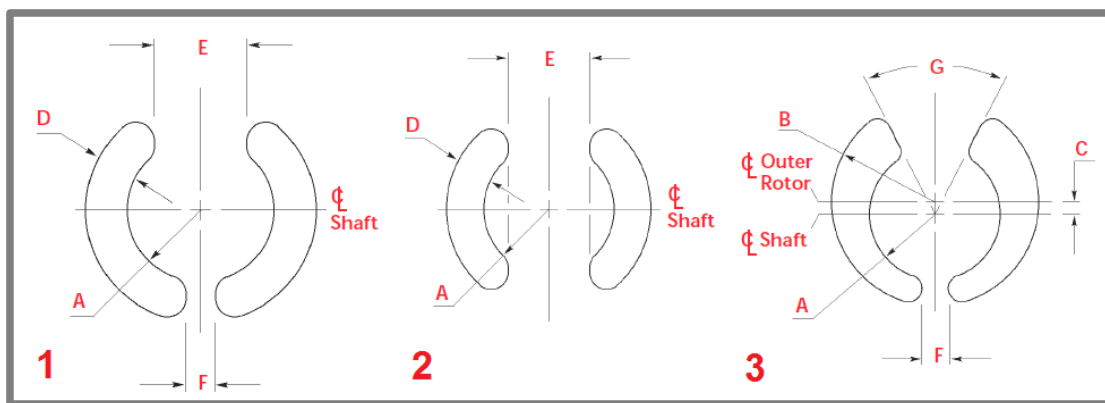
Gerotor s reverzací pomocí opásané pružiny [11]
